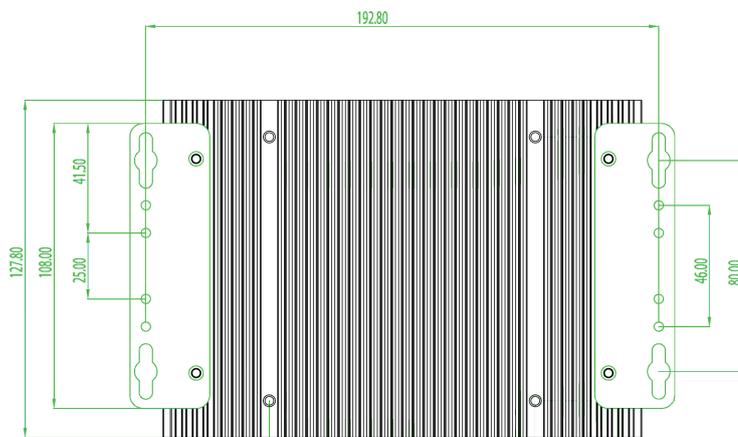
Platzbedarf (in mm) bei Wandmontage
